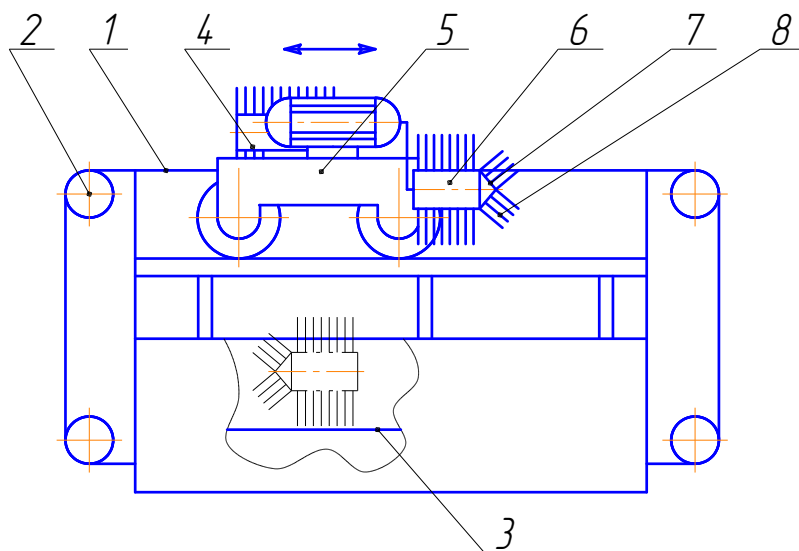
Кормораздатчик 1 – конвейер ленточный бесконечный; 2 – барабан; 3 – кормушка; 4 – сбрасыватель; 5 – тележка; 6 – цилиндр; 7 – конус; 8 – шипы;
